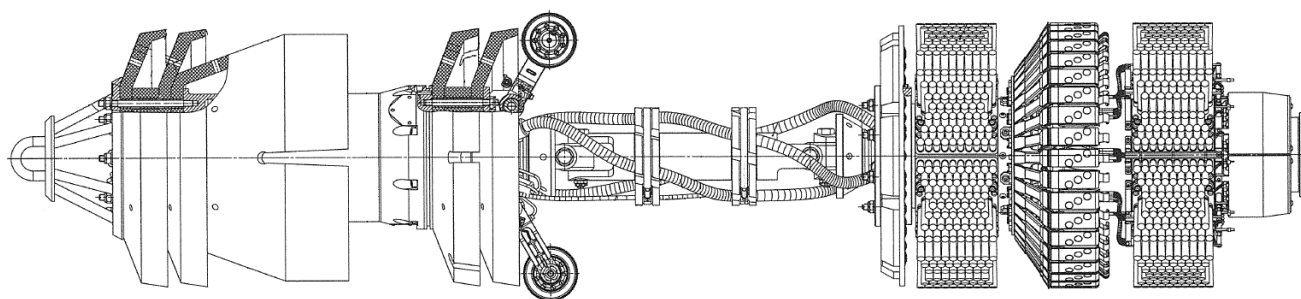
Чертеж общего вида дефектоскопа внутритрубного магнитного 16-MCK.00-00.000-00 и 20-MCK.01-00.000-01
